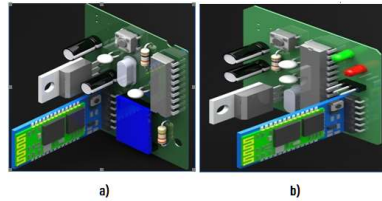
a) Diseño CAD del circuito emisor; b) diseño CAD del circuito receptor.
